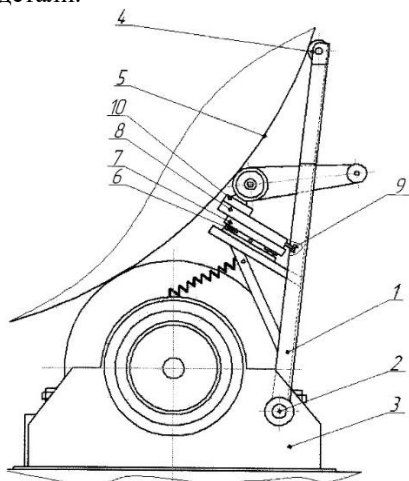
Станок для обработки бандажей: 1- подпружиненный кронштейн; 2- шарниры; 3- корпуса подшипников опорных роликов; 4- копирующий ролик; 5- бандаж; 6- сдвоенные рельсовые направляющие качения; 7- продольный суппорт; 8- каретка; 9- регулировочный винт; 10- обрабатывающий узел [6]
